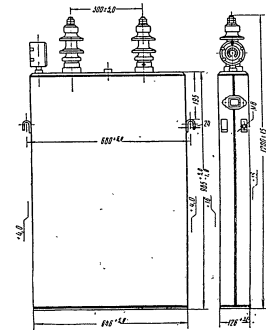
Габаритно-установочные размеры конденсатора типа КПМ 0,6-50-1
